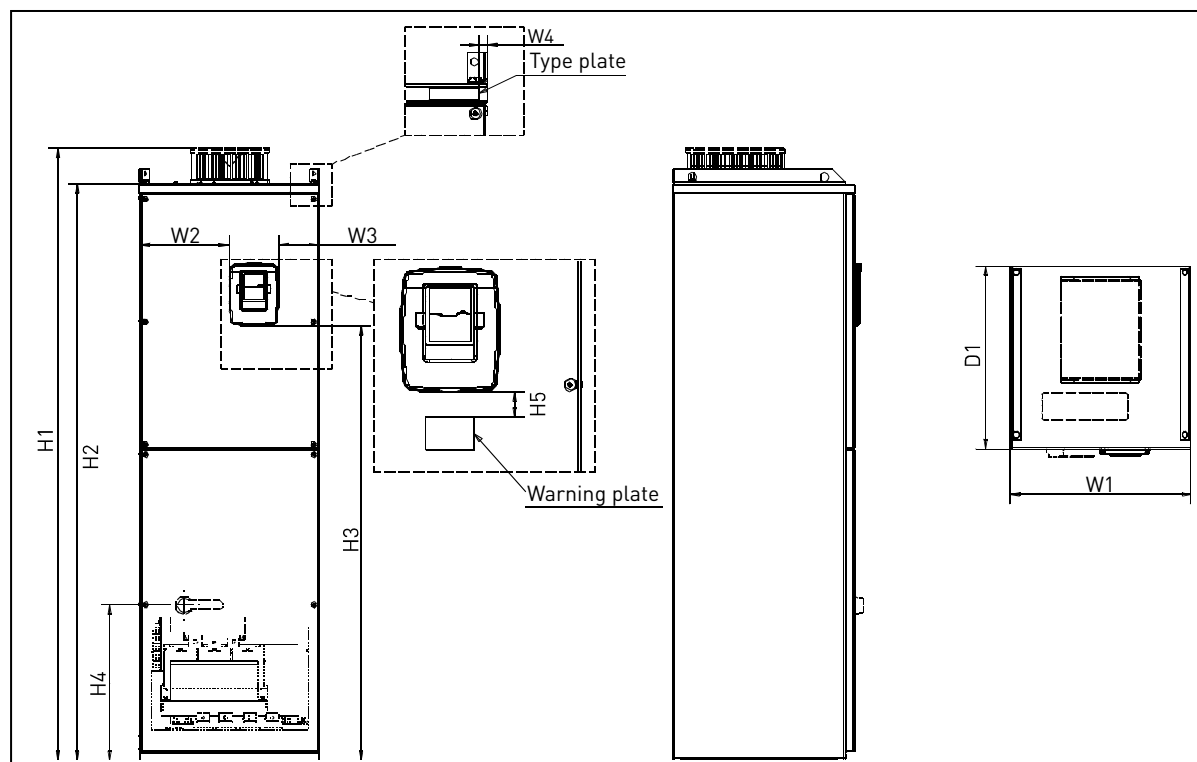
Габариты преобразователей частоты Vacon NX, типоразмеры FR10 и FR11 (напольного исполнения)
